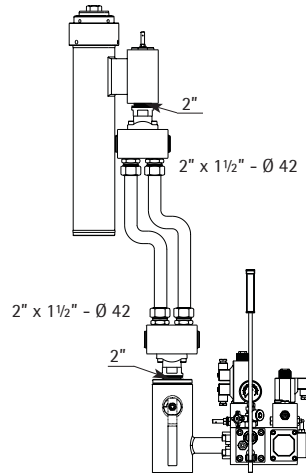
Collegamento con n° 2 Tubi rigidi Ø 42
